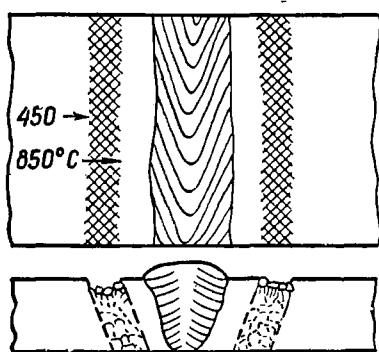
Схема межкристаллитной коррозии в основном металле под воздействием сварочного нагрева.
